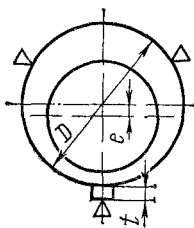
Оправки для обработки эксцентриковых заготовок:
